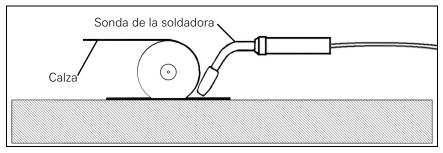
Colocación de la calza del collarín con soldadura
